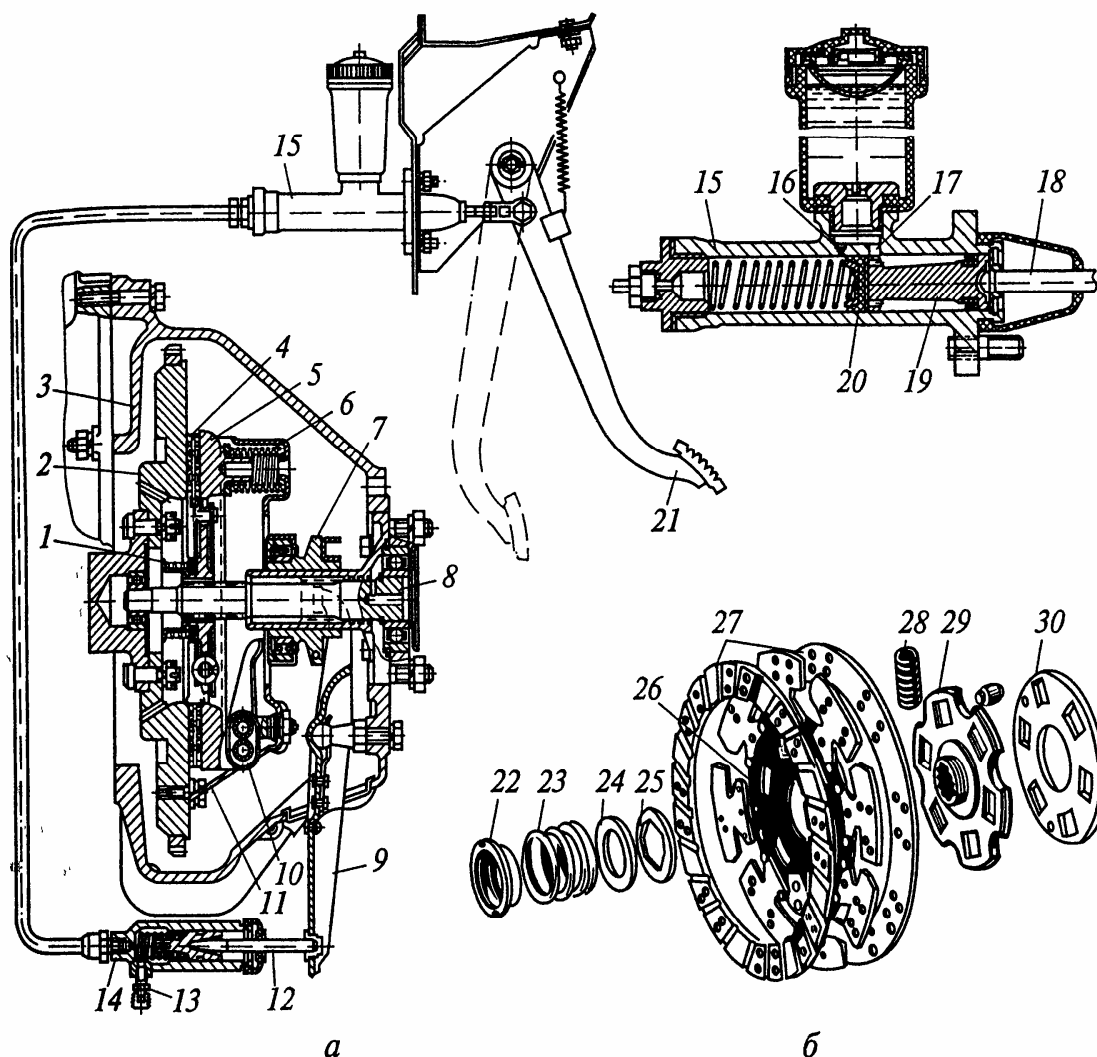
Сцепление, привод (а) и детали сцепления (б) легковых автомобилей ГАЗ:
